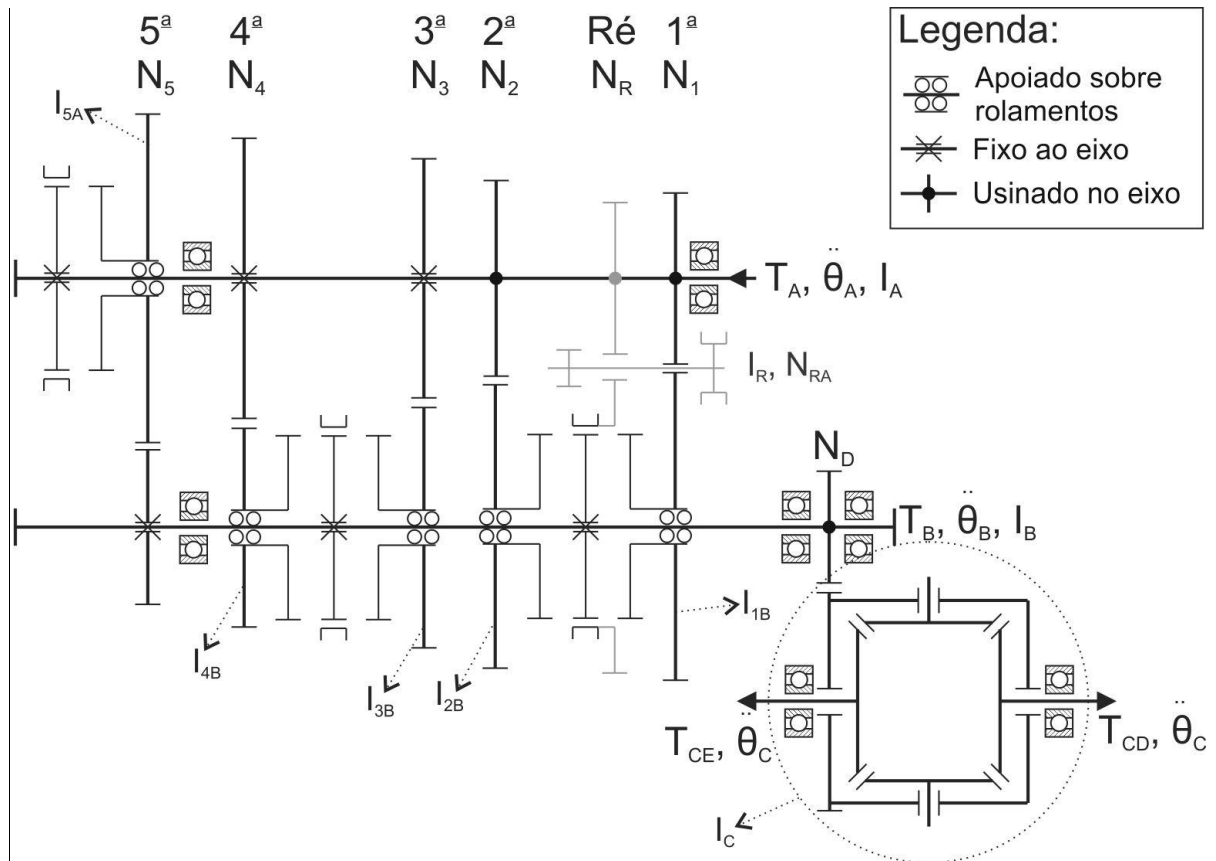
Esquema da transmissão manual de 5 velocidades de carro de passeio (VW MQ 5-speed manual passenger car gearbox).
